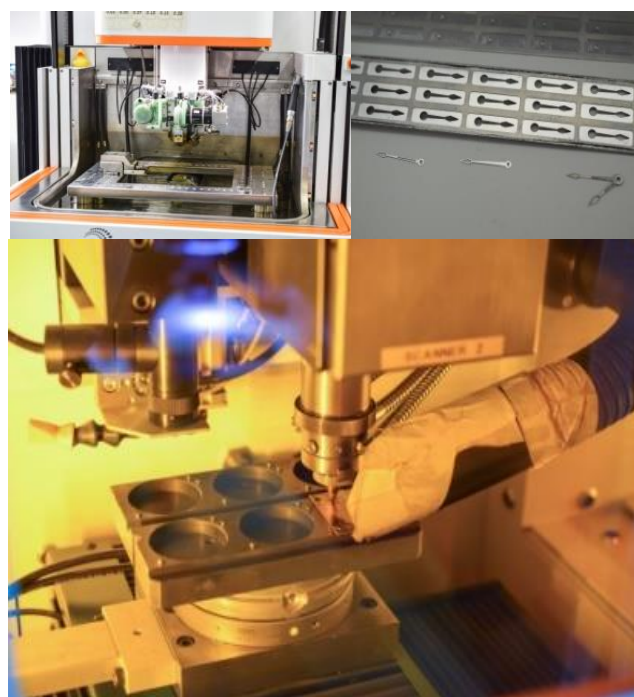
Корпуси след обработка на центри Kern Micro-technik, Rapid Done [5,6]
